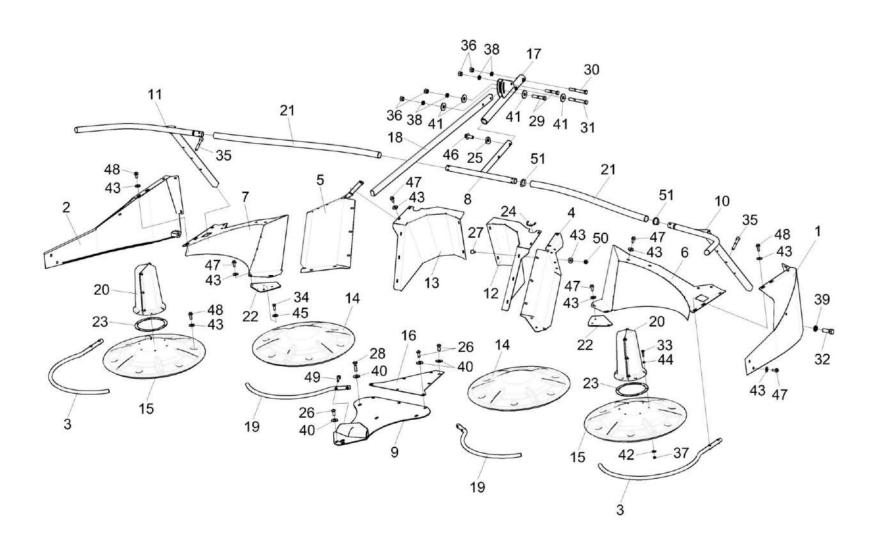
Установка ограждений ЖКС-45-0100080 (вид спереди)
